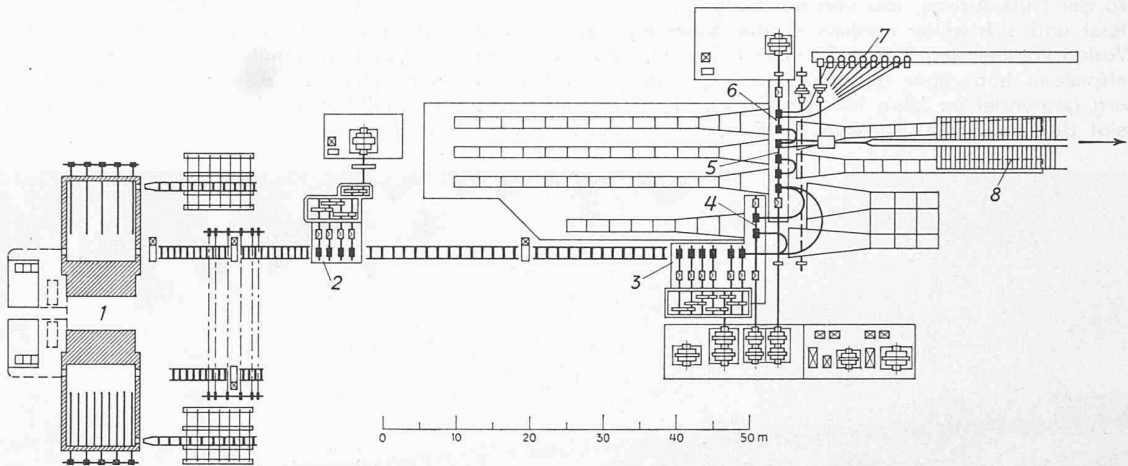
Anordnung des Drahtwalzwerks in Belval. 1 Öfen, 2 und 3 kontinuierliche Strassen, 4 Zwischenstrasse, 5 Fertigstrecke, 6 Drahtgerüste, 7 Haspel, 8 Kühlbetten
